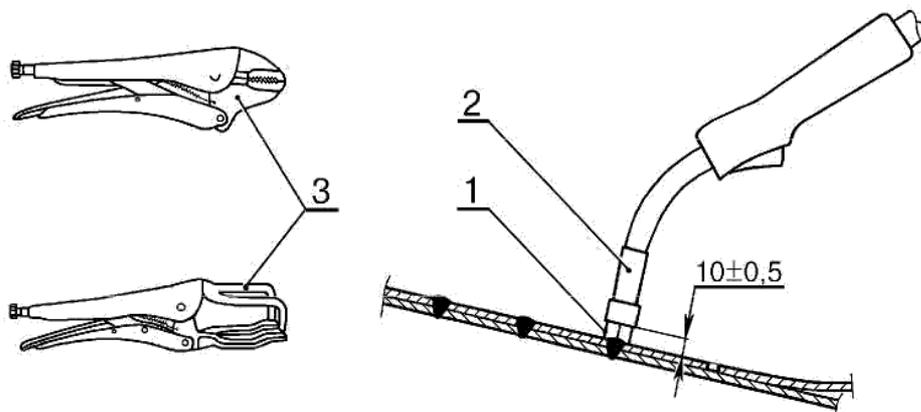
Выполнение сварочной точки. 1 - опорные ножки газового сопла; 2 - газовое сопло сварочного аппарата; 3 - зажимные клещи
